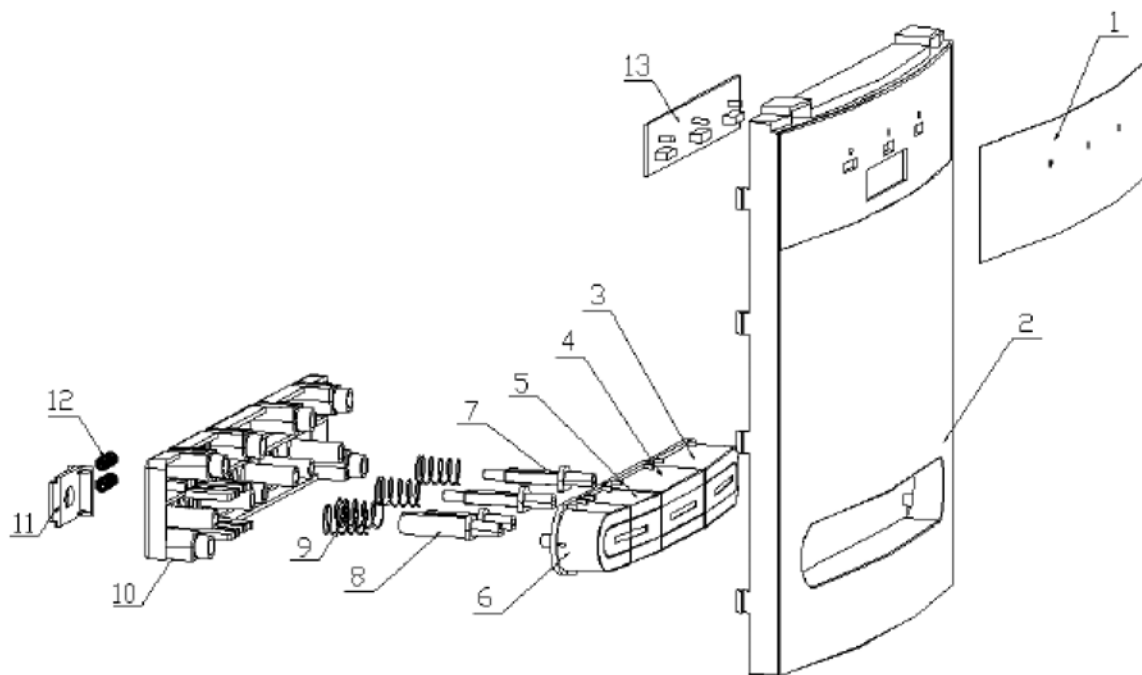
Assemblage des robinets et du panneau d'accès frontal
